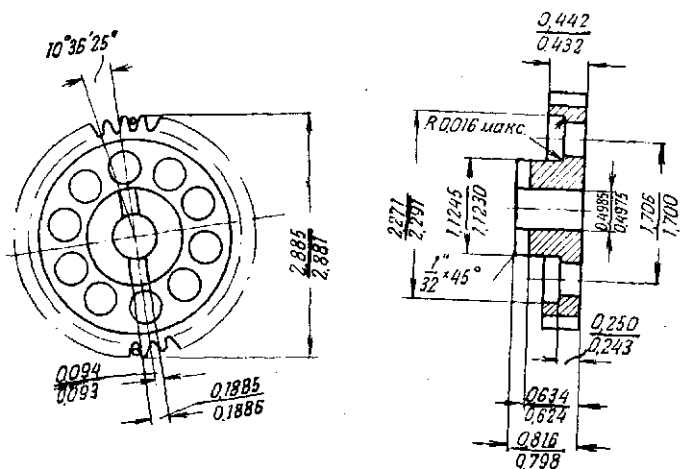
Чертежи ведомой шестеренки (Клаузер)
